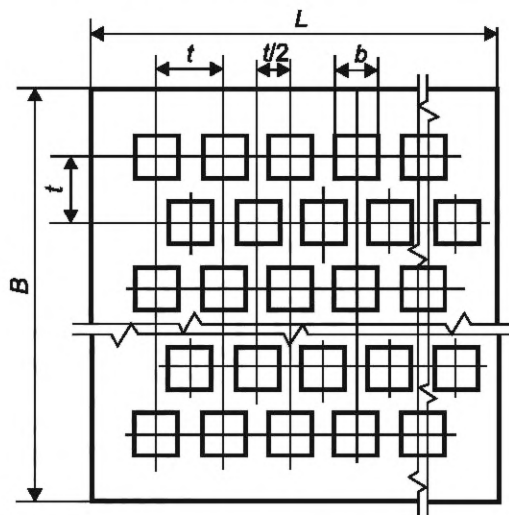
Размеры квадратных отверстий и диаметры круглых отверстий
